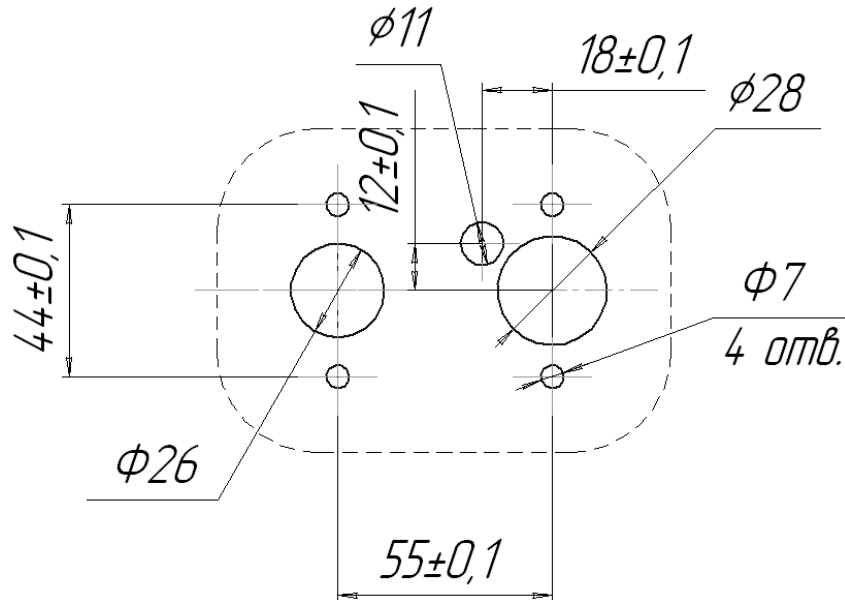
Монтажные отверстия для установки нагревателя
